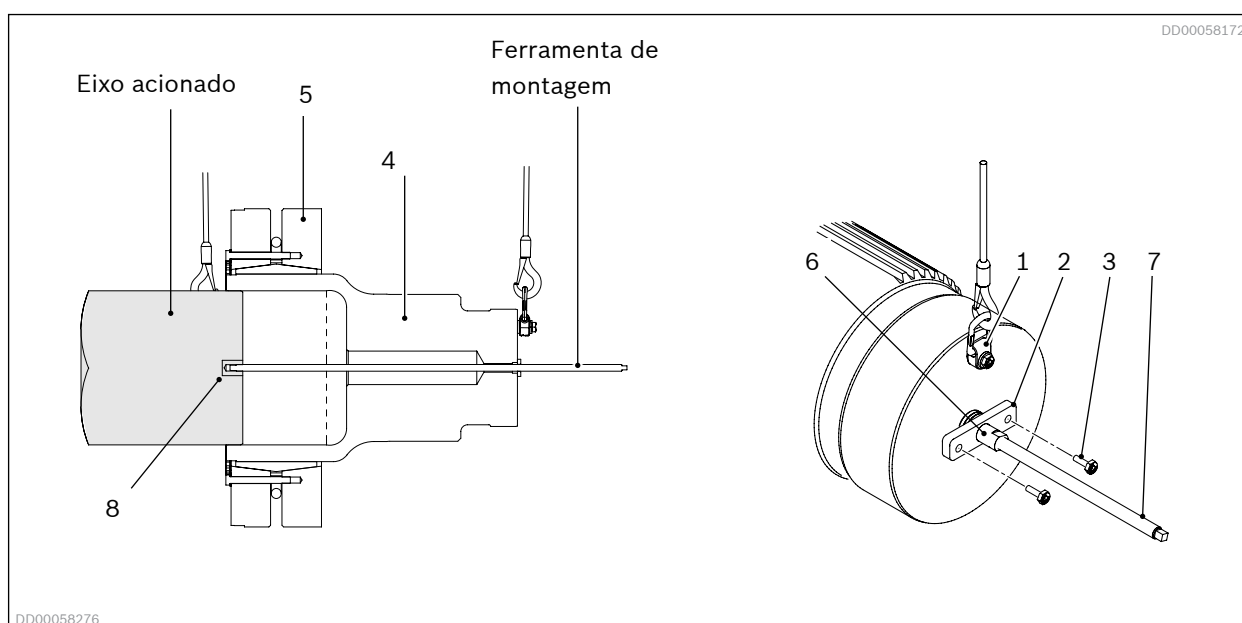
Montagem do adaptador de acoplamento com a ferramenta de montagem
